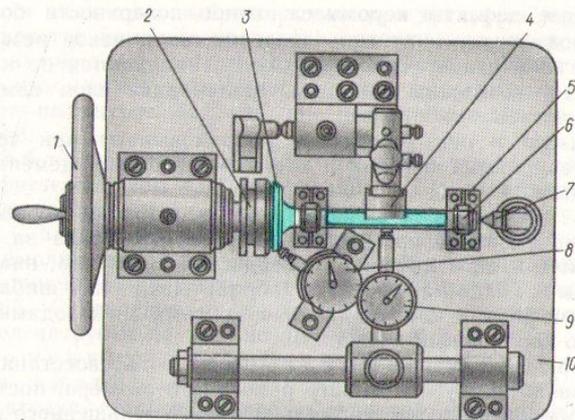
Приспособление для проверки биения рабочей фаски и стержня клапана: 1 — маховик; 2 — палец; 3 — клапан; 4 — прижим; 5 — призма; 6 — ролик; 7 — упор; 8 и 9 — индикаторы; 10 — плита.
